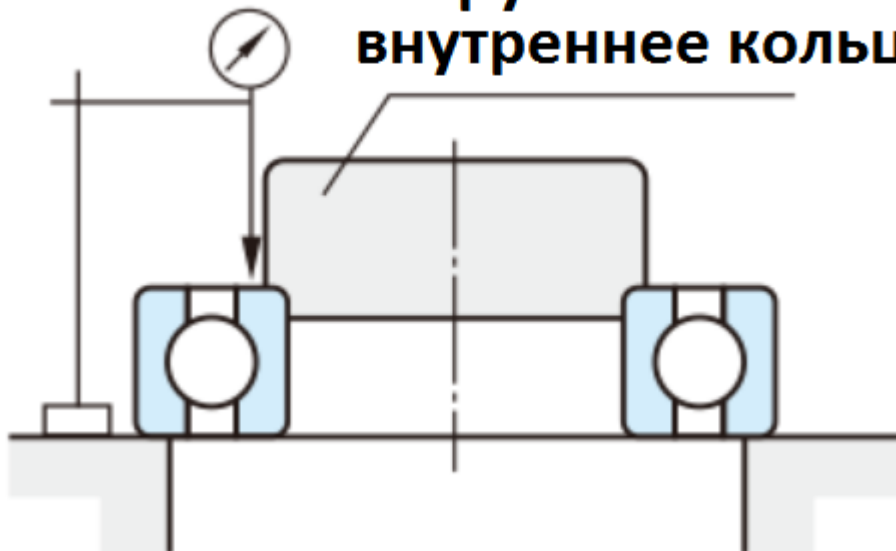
Торцевое биение внутреннего кольца подшипника в сборе. Внутренне кольцо проворачивается на полный оборот. Иллюстрация "Коуро"
